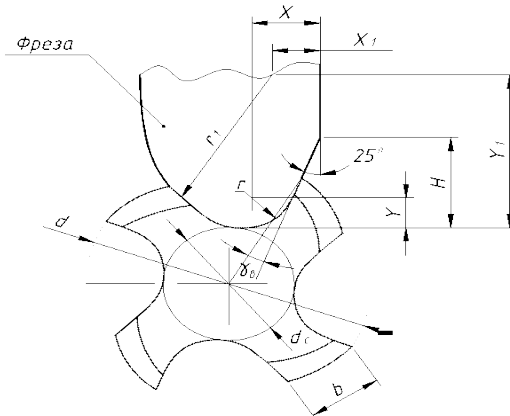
Профиль фасонной фрезы для формирования поперечного сечения мерного инструмента
